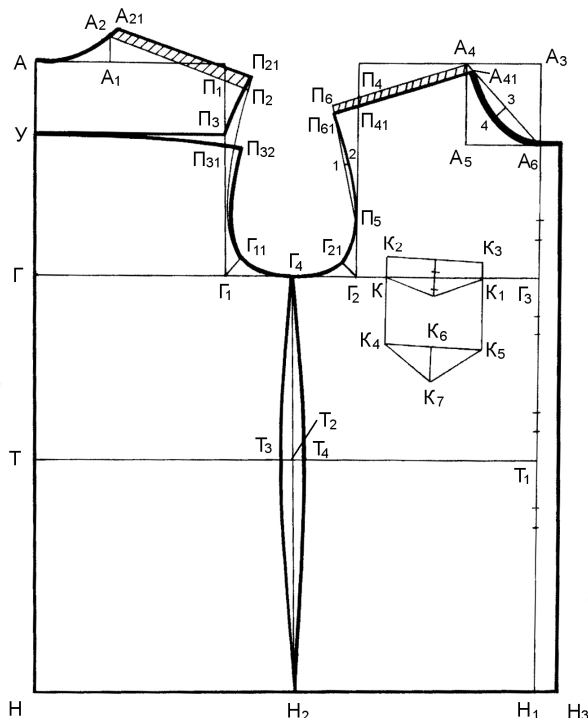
Креслення базової конструкції пілочки і спинки чоловічої сорочки
